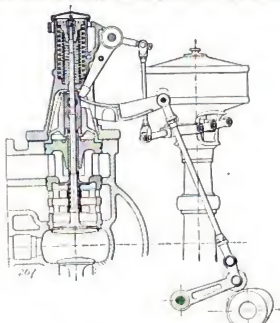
Z. A.: Der neue Deutzer Motor M. 11.
